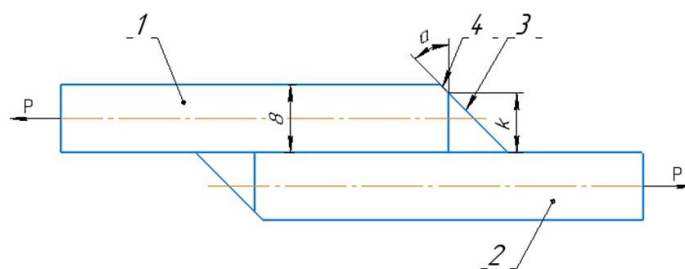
Усовершенствованное сварное нахлесточное соединение
